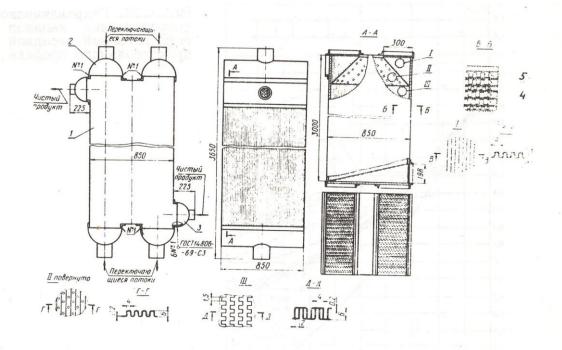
Трехпоточный реверсивный пластинчаторебристый теплообменник I - пакет; 2,3 -коллекторы; 4 - ребра типа I2/2; 5 - ребра типа 4/2.
